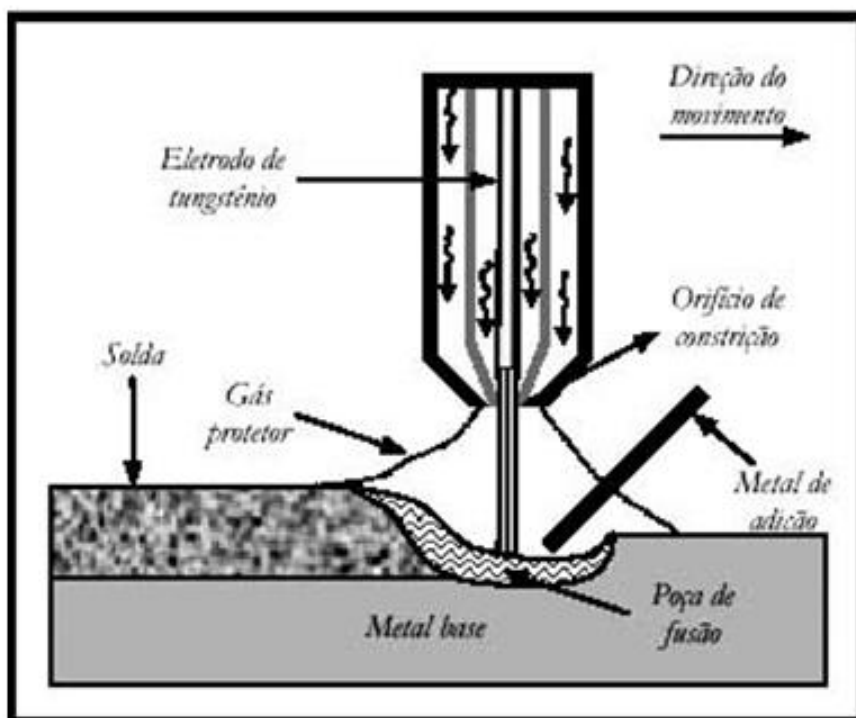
Esquema do processo de soldagem a arco com plasma.
